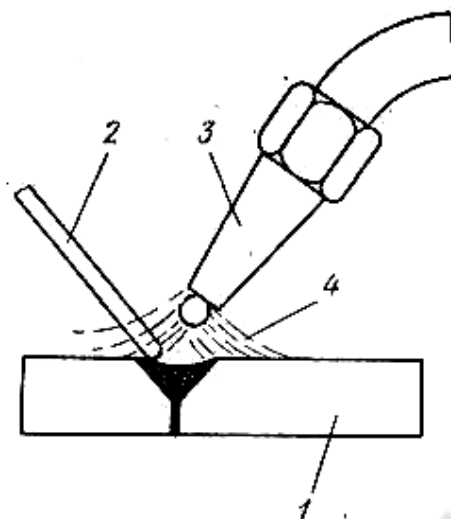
Схема газовой сварки: 1 – свариваемый материал; 2 – присадочный пруток; 3 – наконечник газовой горелки; 4 – газовое пламя
